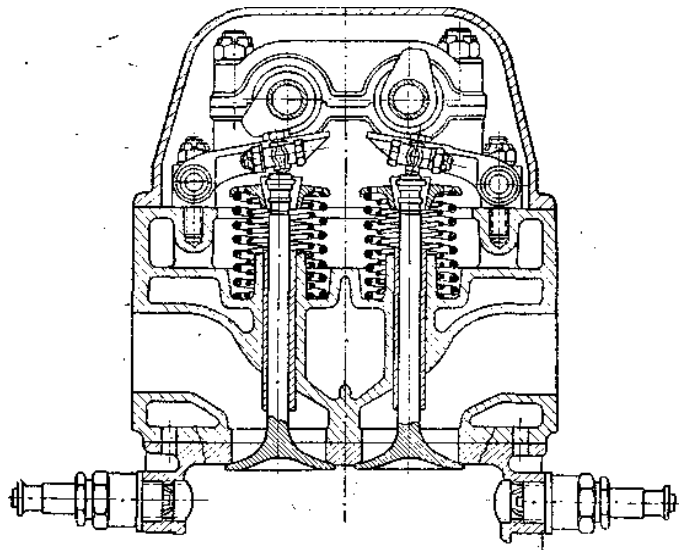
Клапанный механизм с двумя кулачковыми валами
